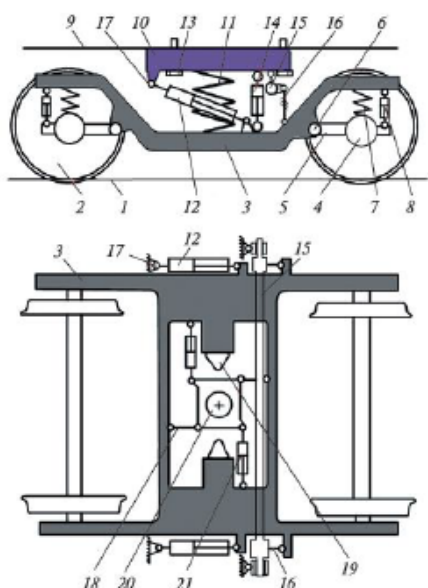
Кинематическая схема моторной тележки (вид сбоку и сверху): 1 – уровень головок рельсов; 2 – колесная пара; 3 – сварная рама тележки; 4 – букса колесной пары; 5 – разъемный (разрезной) буксовый рычаг (балансир) 1-й ступени рессорного подвешивания; 6 – сайлент-блок буксового рычага 1-й ступени рессорного подвешивания; 7 – цилиндрическая пружина 1-й ступени рессорного подвешивания; 8 – демпфер гашения вертикальных колебаний 1-й ступени рессорного подвешивания;
